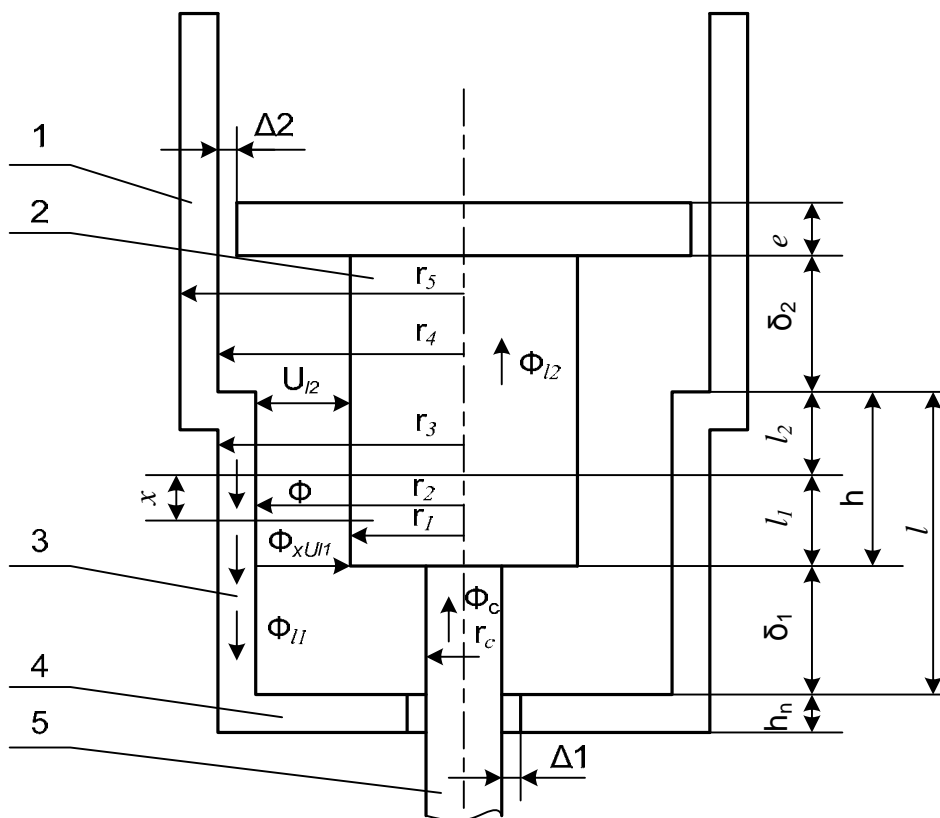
Магнитная цепь ЛЭМД с двумя рабочими зазорами, комбинированным якорем и ферромагнитным направляющим корпусом:
